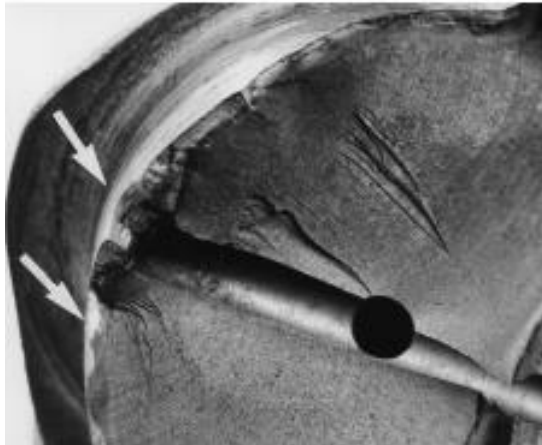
Cambota partida, após a reconstrução, setas na zona soldada. (Heyes, 1998)
